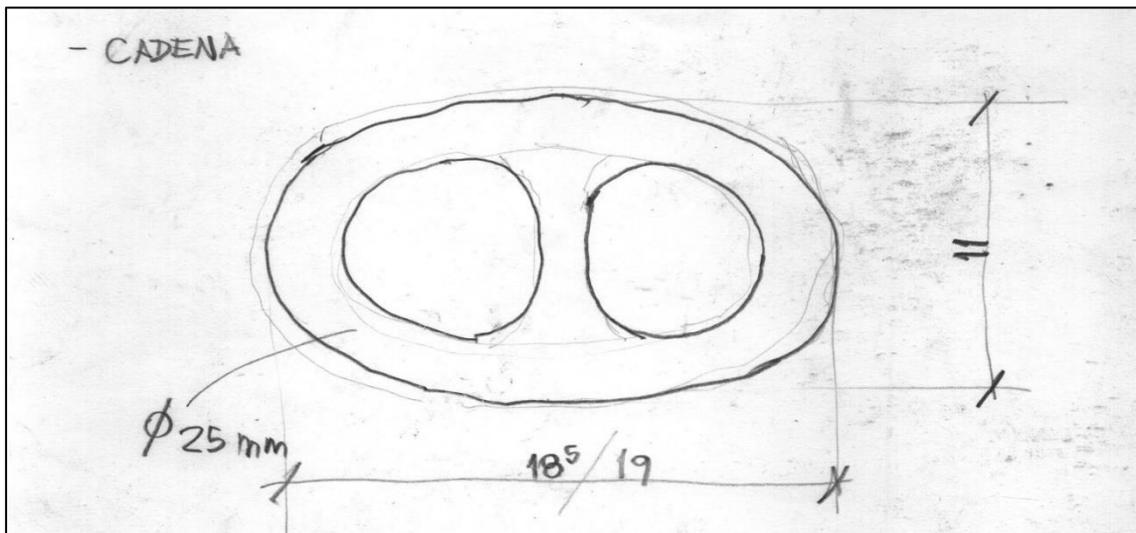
Detalles de un eslabón del fragmento de cadena. Croquis C.Murray
